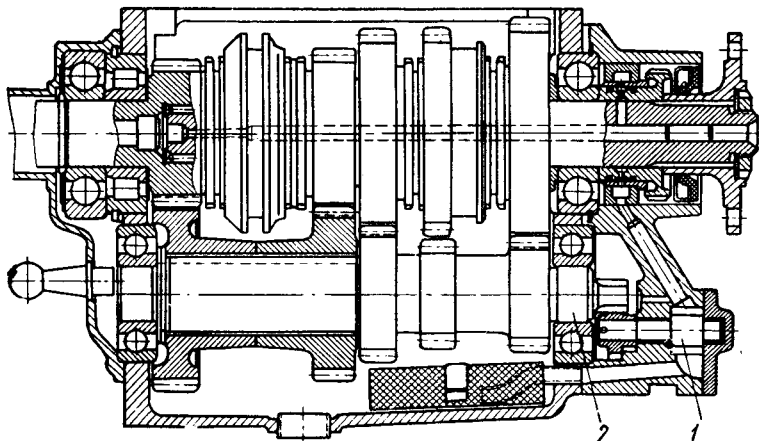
Четырехступенчатая коробка передач спортивного автомобиля Мерседес Бенц типа 300SL с передним расположением двигателя.
